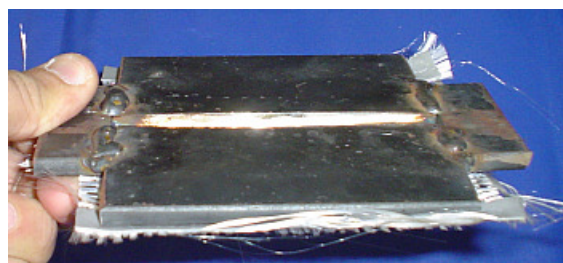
Suporte de solda montado na chapa pronto para a soldagem.
